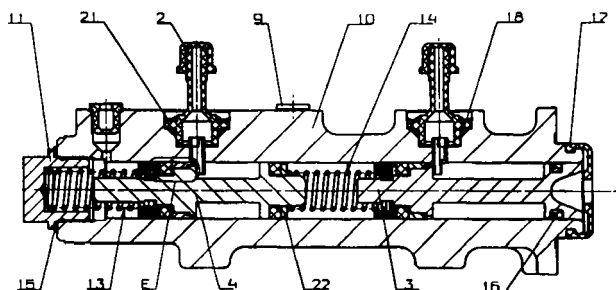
Сдвоенный главный цилиндр автомобилей ВАЗ Кор. "Фенекс"
